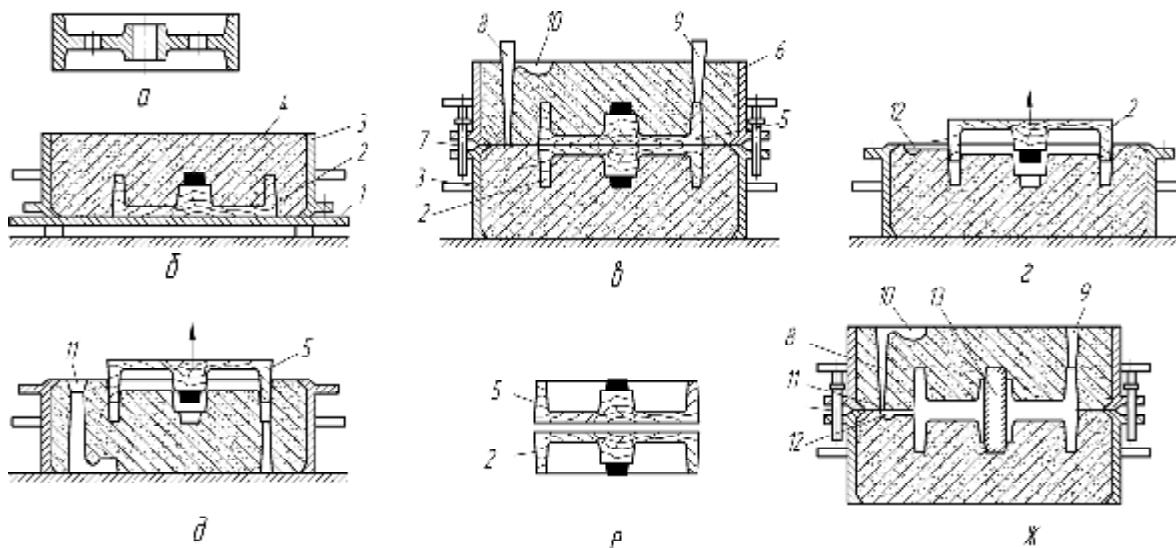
Форма для изготовления шкива, выполненная в двух опоках:
